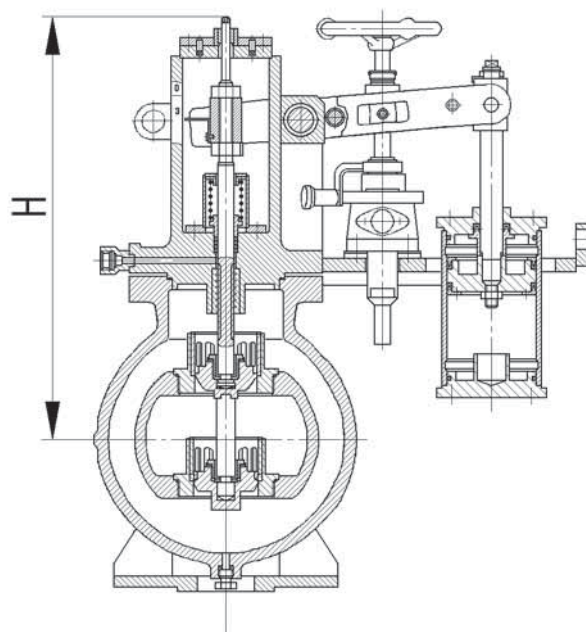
Клапан регулирующий проходной фланцевый с гидроприводом и ручным управлением
